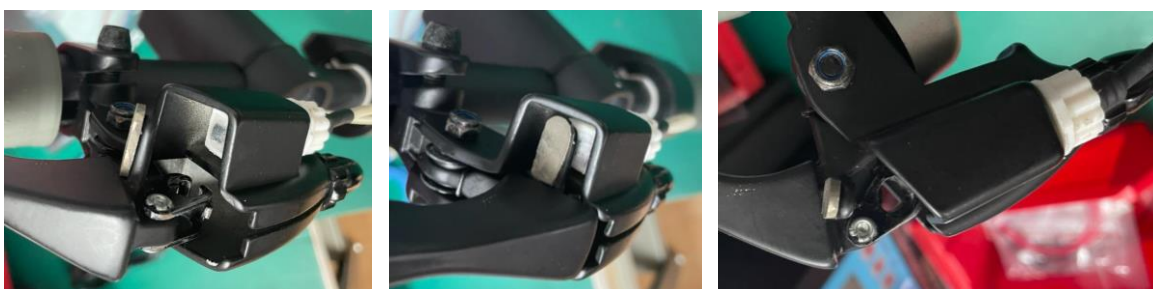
Resultado del mecanizado y montaje del imán en el sensor de frenado
